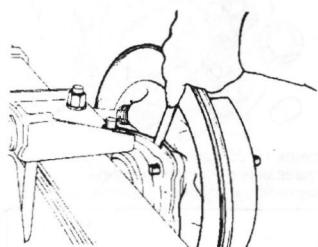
Используйте толщиномер для измерения зазора между корпусом подшипника и кожухом моста
